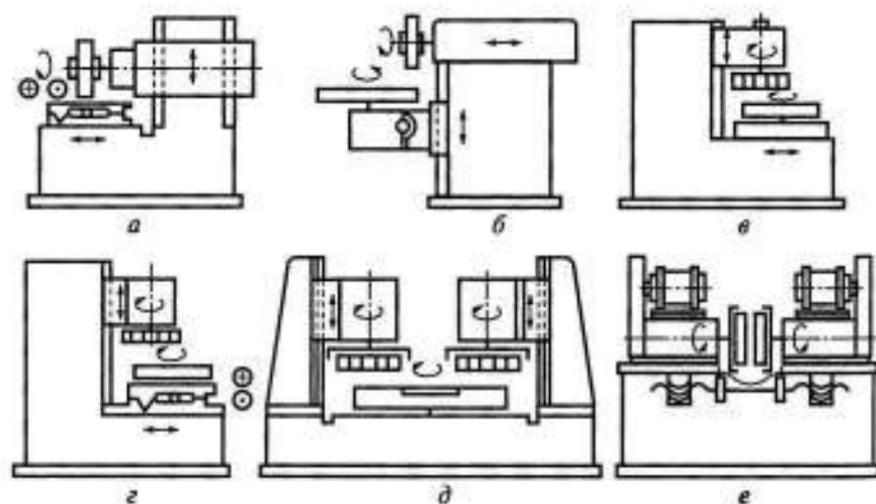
Схема обработки на плоскошлифовальных станках с обозначением движений:
